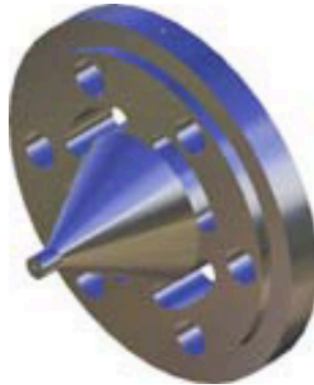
Mandril semejante al de la propuesta 1 pero con un ángulo a la salida más abierto.
